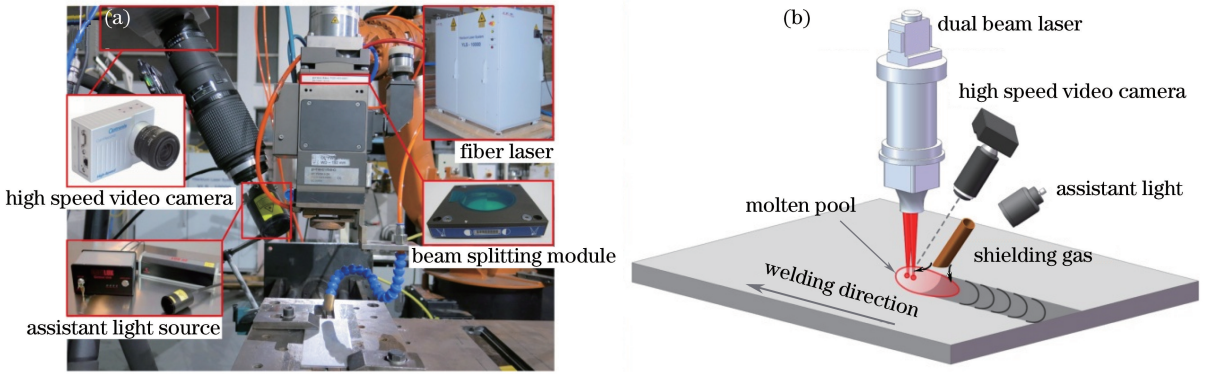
焊接试验装置。(a) 试验设备；(b) 焊接过程示意图
